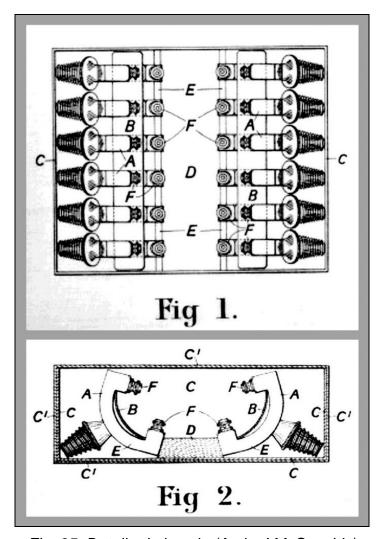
Detalle de la caja (Arch. J.M. Sanchis)
